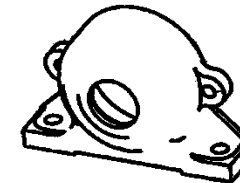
Корпус подшипника КИР.02.0.1009
